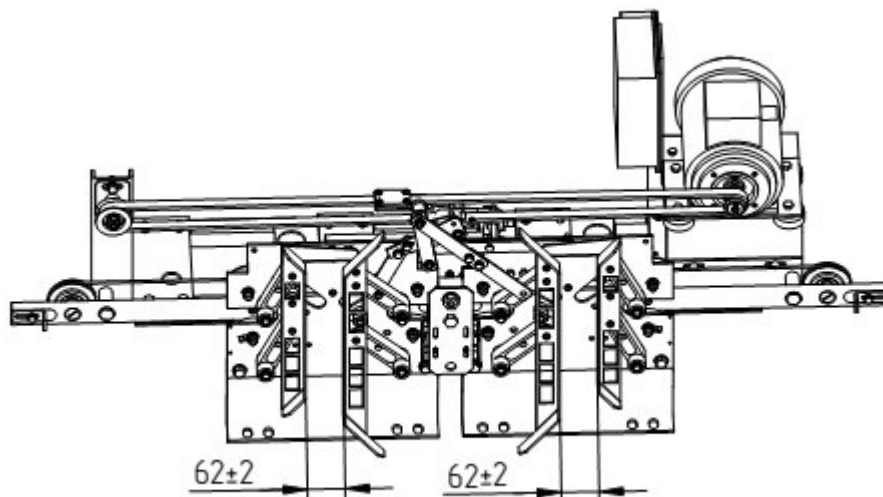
Привод 0463Б.03.45.000, 0610Б.03.45.000 (см. ФБИР.483310.001 ДР39)
